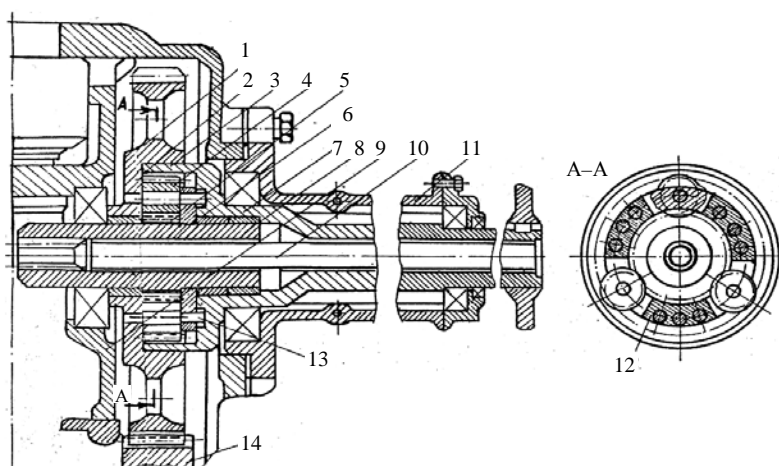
Упруго-эластичный привод трактора МТЗ-80: 1 – колесо; 2 – планетарный механизм; 3, 5, 14 – шестерня; 4 – сателлит; 6 – водило; 7 – полуось; 8 – вал; 9 – корпус; 10 – торсионный вал; 11 – рукав; 12 – перемычка; 13 – ось
